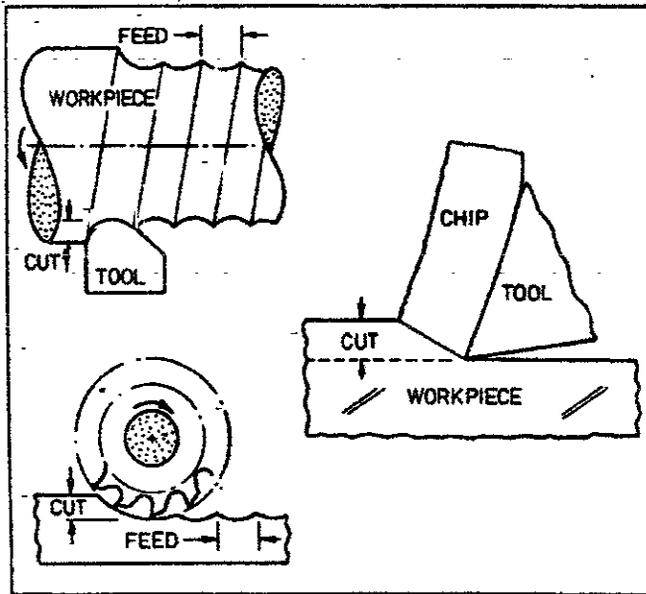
Maquinado: torneado (izquierda arriba), fresado (abajo) la herramienta de corte debe tener la información del filo y dureza para desprender viruta la superficie de la pieza de trabajo. (Tomada de la referencia [1]).
